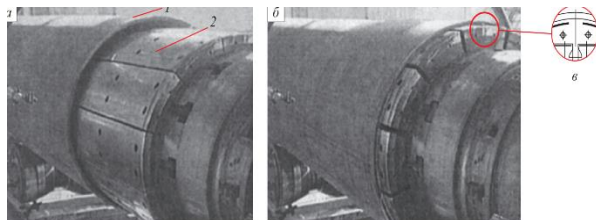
Загальний вигляд ТВД в експандері: *a* – підготовка труби до операції; *б* – операція експандування; *в* – розташування зварного шва;
